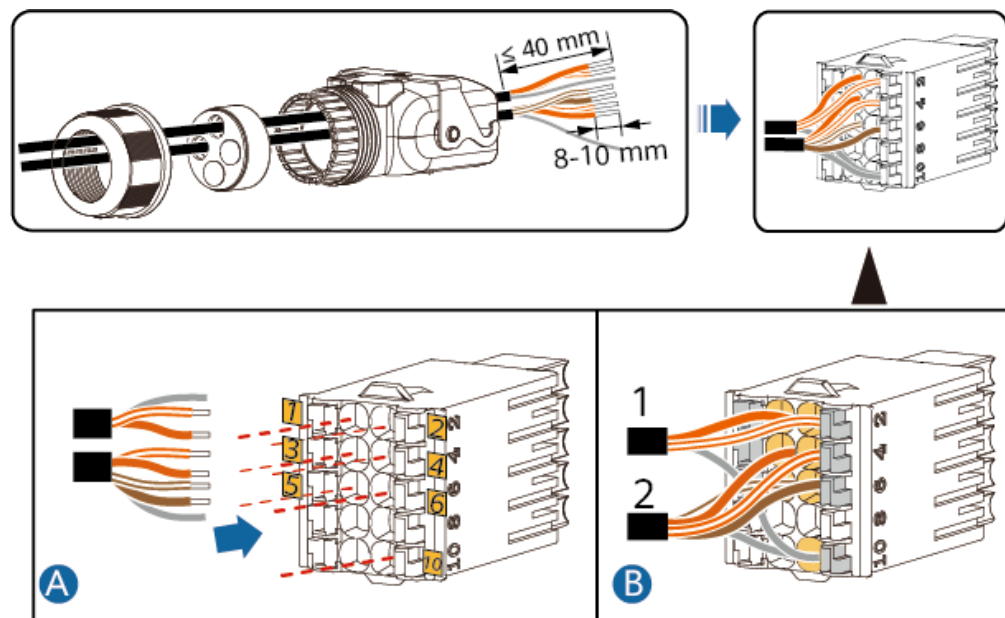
Installazione del cavo (collegamento a SmartAssistant)
